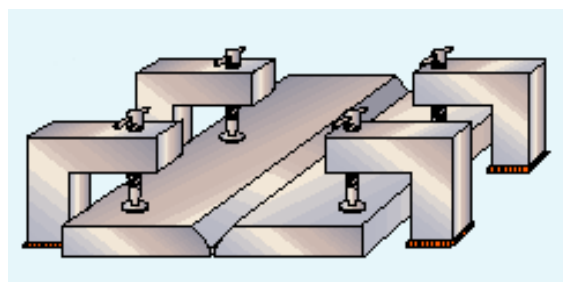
Restrictores de movimiento en una soldadura a tope ²³
